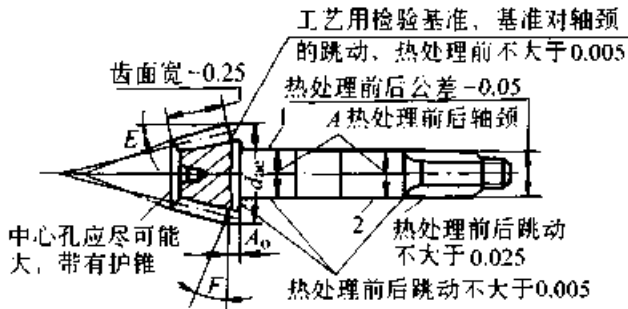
锥齿轮轴的轮坯公差
